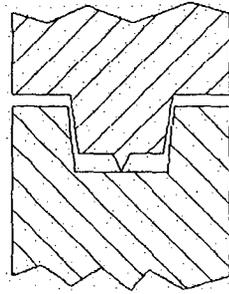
União macho e fêmea para soldagem ultrassônica.
